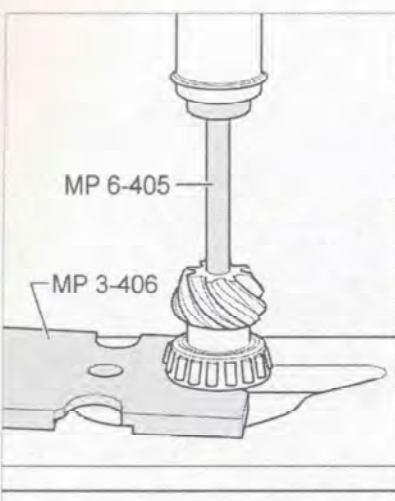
Напрессуйте внутреннюю обойму большого роликоподшипника до упора с помощью специального инструмента.
